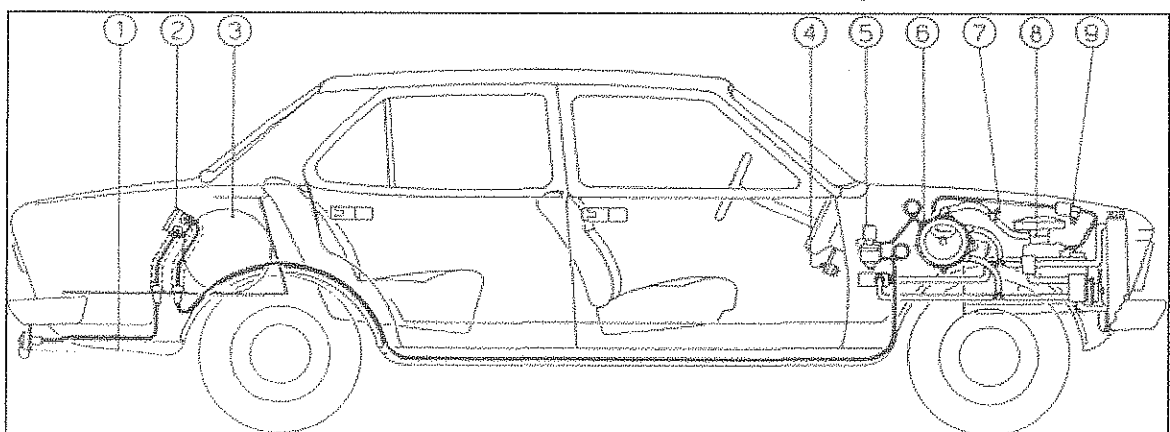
Esquema del montaje componentes instalación GLP.
